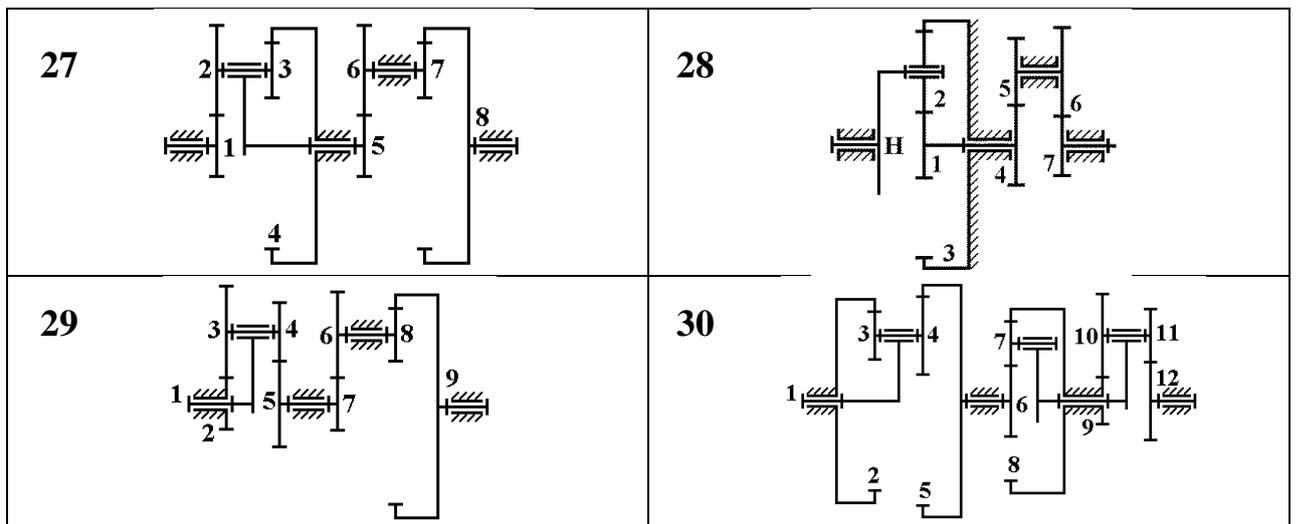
Схемы многосменных зубчатых механизмов с планетарной ступенью
